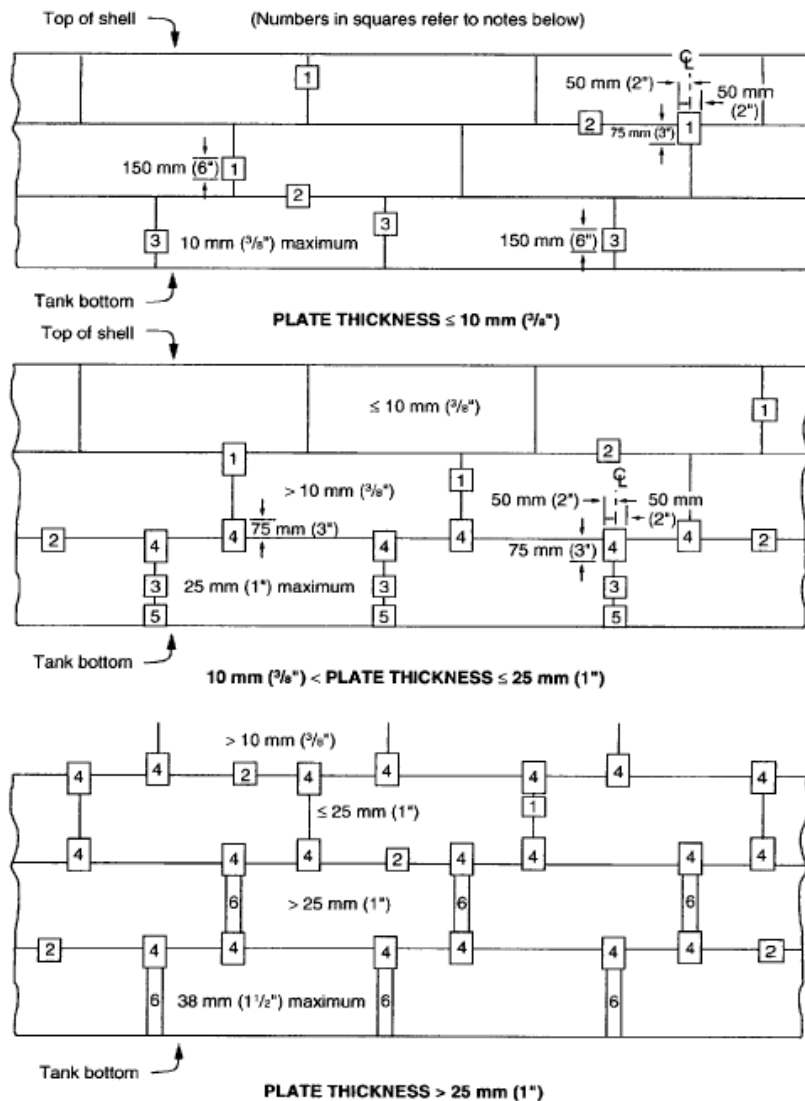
1 Requerimientos de examen radiográfico para juntas soldadas en la pared del tanque
